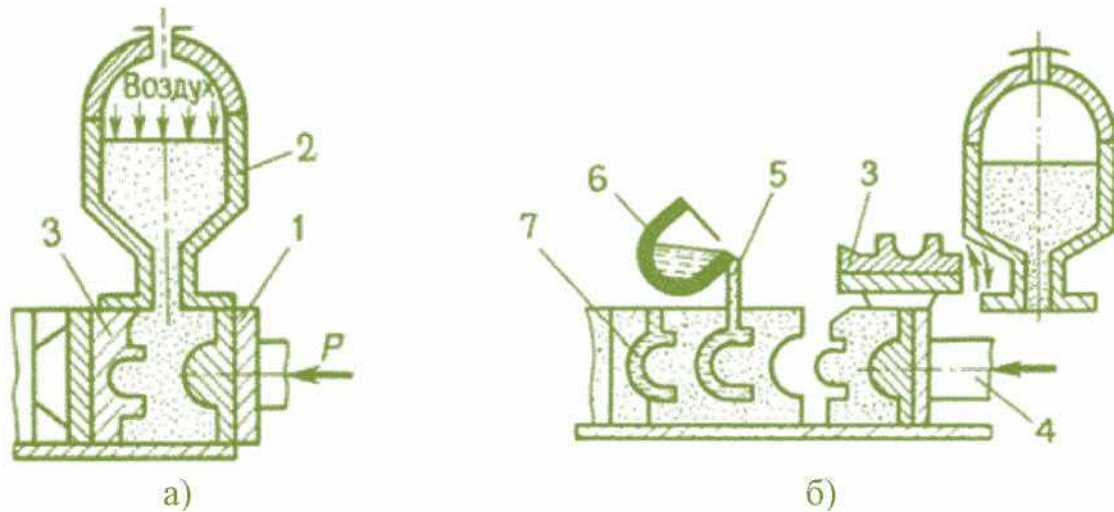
Схема виготовлення безопочних ливарних форм
